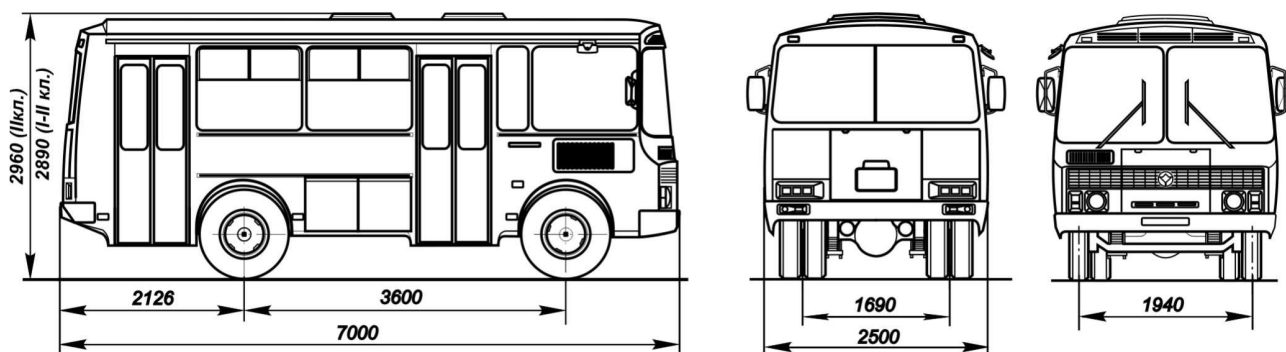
Габаритные размеры автобуса ПАЗ-32054-04
